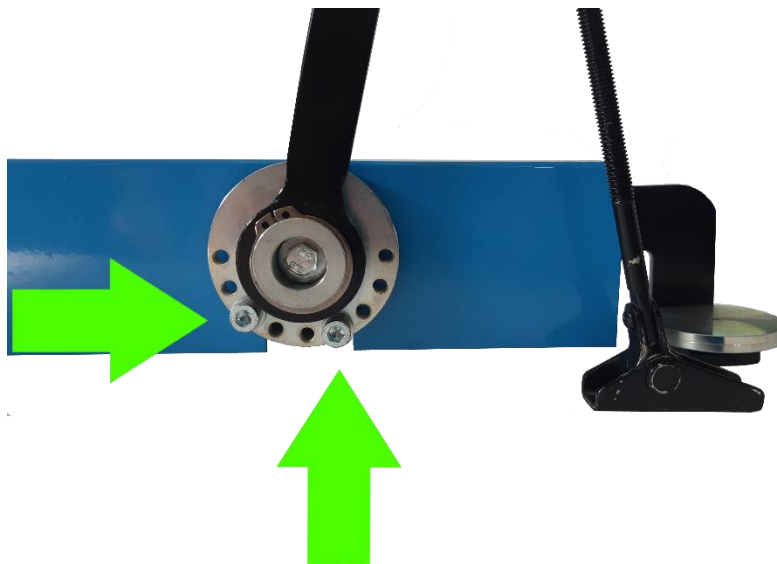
Viti a brugola da svitare per poter posizionare correttamente il braccetto
